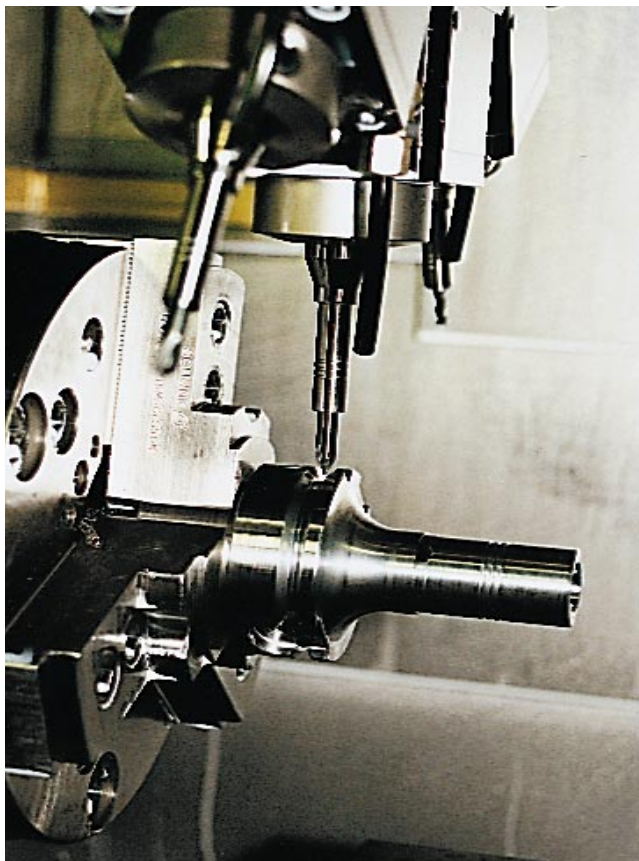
Entgraten eines Werkzeughalters mit schrumpfgespanntem Werkzeug und 6-mm-Verlängerung auf einem Doppelspindel-Drehautomaten.
